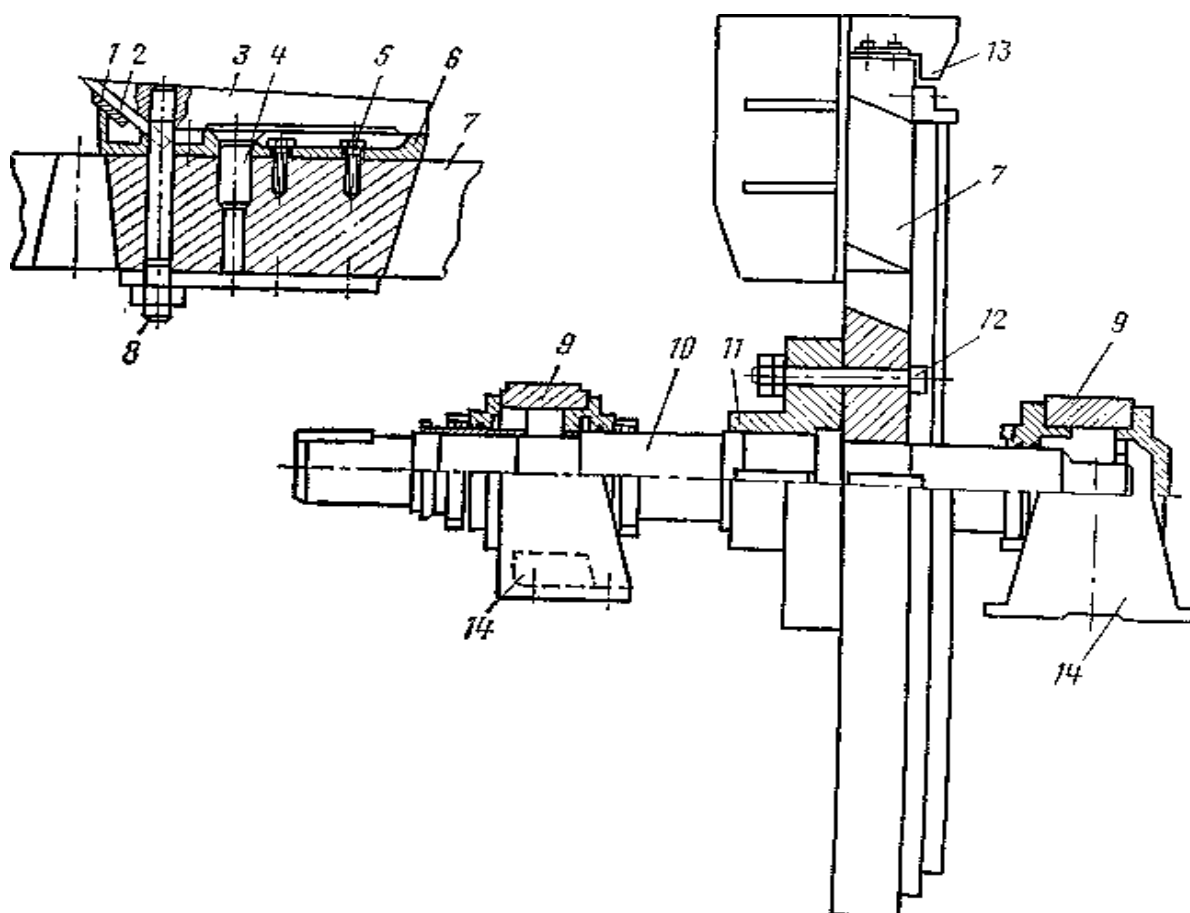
Продольный разрез по ротору рубительной машины «Блэк-Клавзен»: 1 – стружколоматель; 2 – режущий нож; 3 – накладка; 4, 8 – шпилька; 5 – винт; 6 – подкладка; 7 – ножевой диск; 9 – подшипниковая опора; 10 – вал; 11 – фланец; 12 – болт; 13 – лопатка; 14 – корпус подшипника
